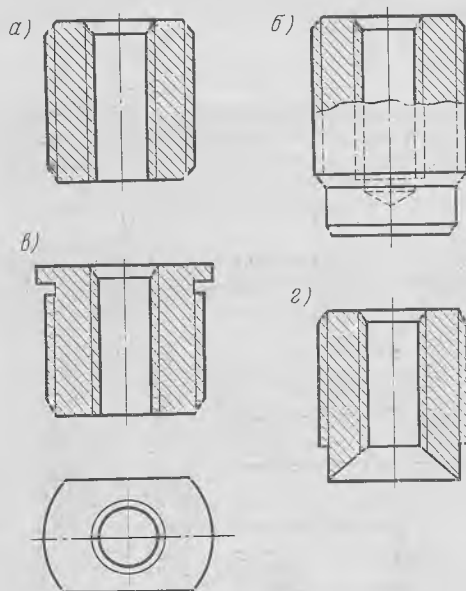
Основные типы свертышей: а — прямой открытый; б — прямой закрытый; в — прямой открытый с буртиком под ключ; г — ступенчатый (под развальцовку одного конца)
